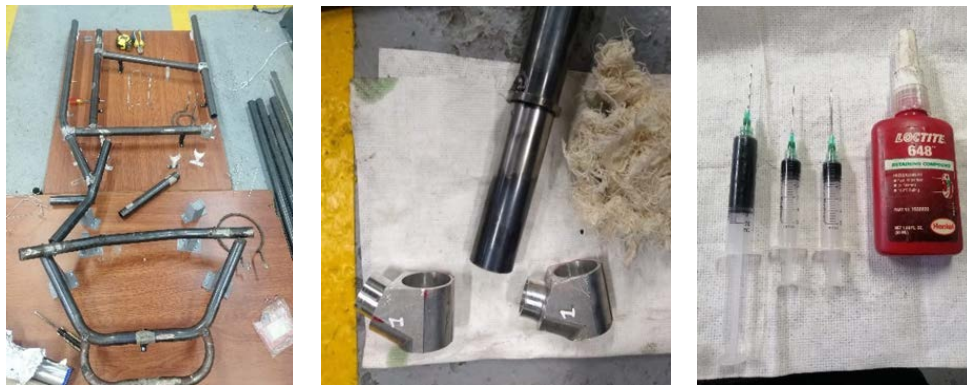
Ensamble de prototipo chasis. Primero se lleva el proceso de unión con adhesivos, y luego las uniones soldadas. Con ayuda de la matriz de soldadura se ubicaron los elementos y las uniones adhesivas
